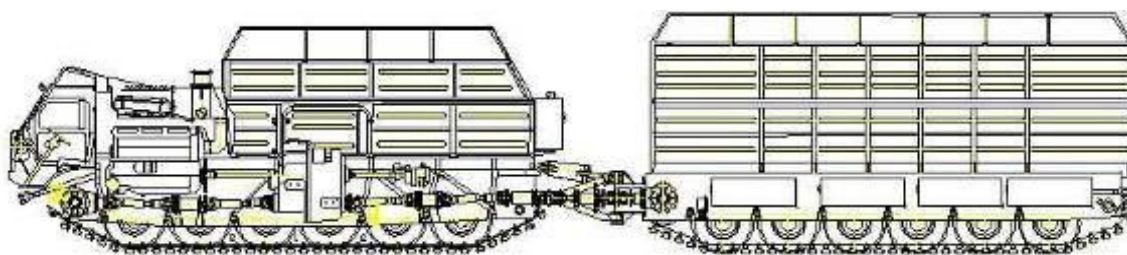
Двухзвенный гусеничный транспортер ДТ-10П в разрезе
